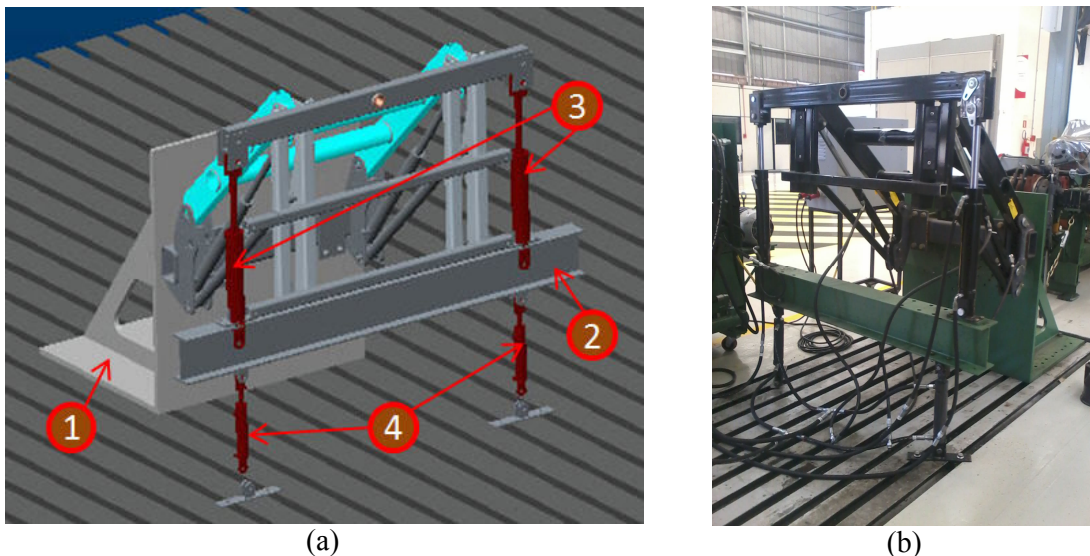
a) Projeto da bancada; b) Início da construção da bancada
